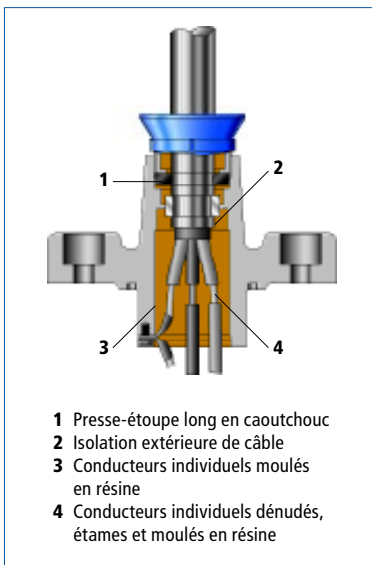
a : Plan en coupe d'un passage de câble parfaitement étanche sur une pompe
